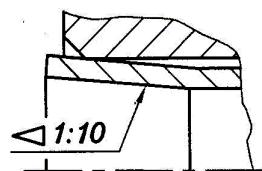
Конічне розвальцовування труби перед зварюванням
